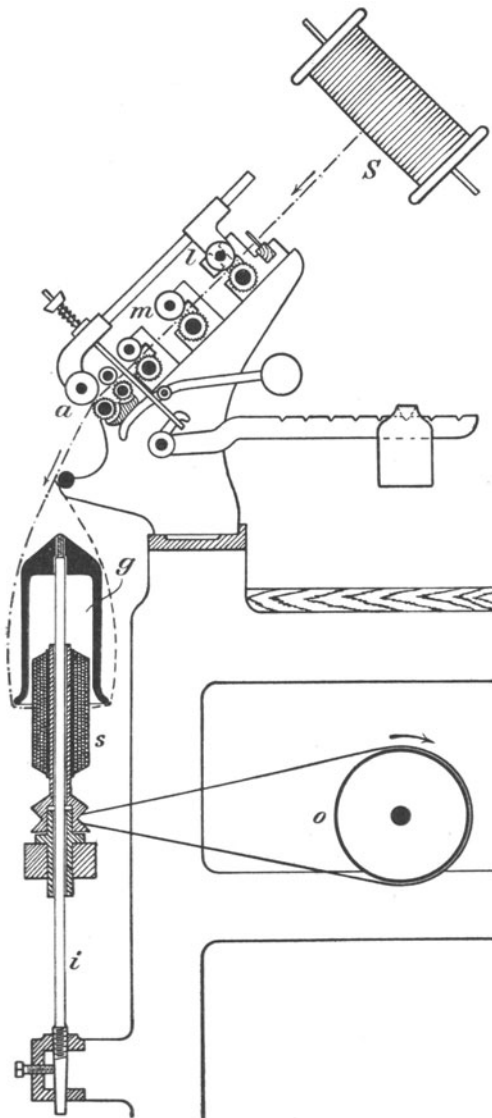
Glockenspinmaschine für Langfaserkammgarne.
